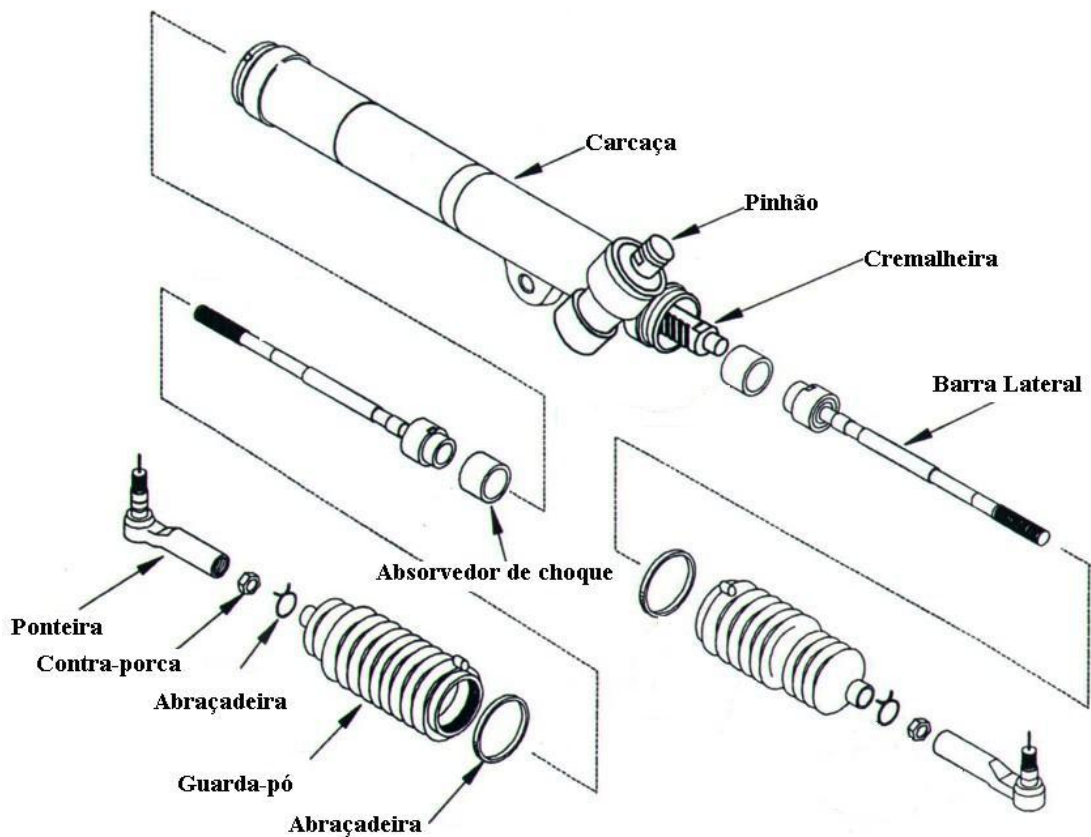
Vista explodida. Fonte: Manual Delphi
